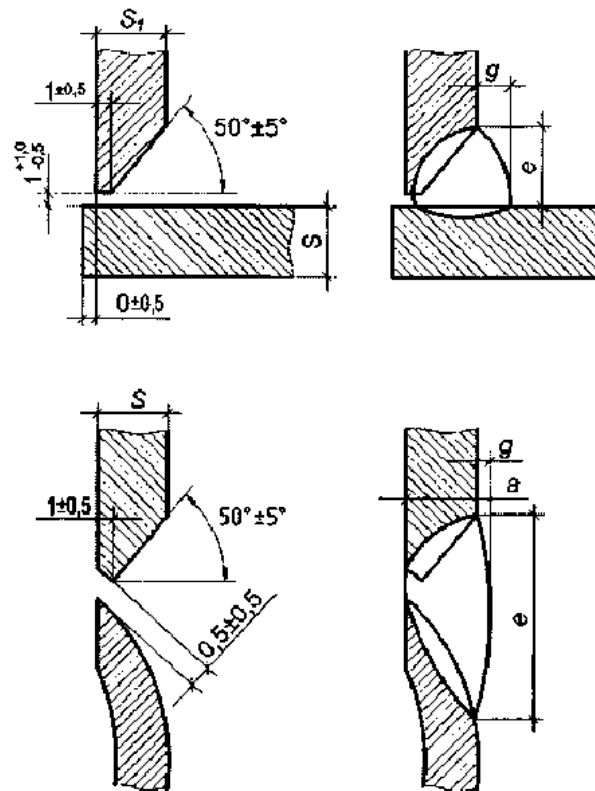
Підготовка кромки кутового з'єднання У19
